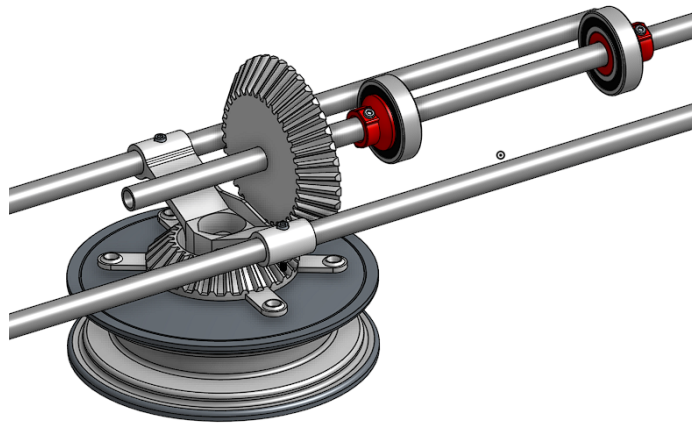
Vista isométrica 2 del ensamblaje de la transmisión con engranajes cónicos con el alternador en Onshape [fuente: elaboración propia]
